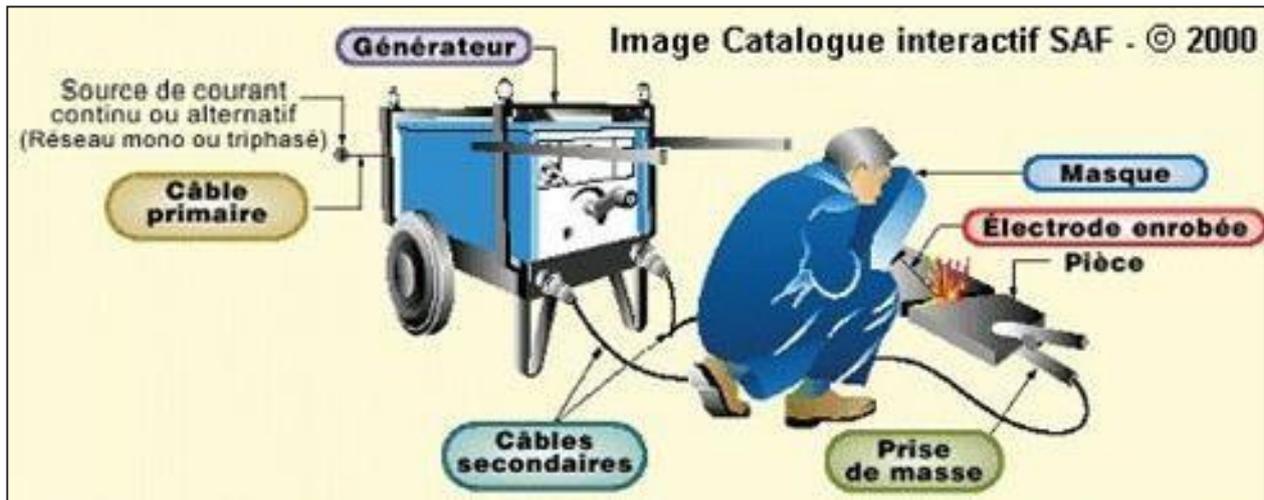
Installation pour soudage à l'électrode enrobée [9]
